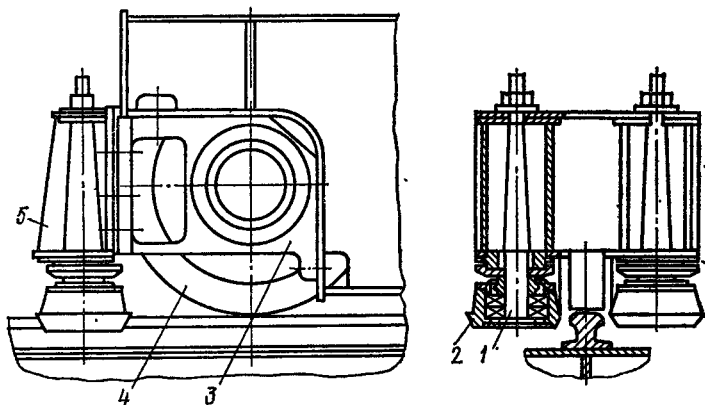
Установка безребордного ходового колеса механизма передвижения мостового крана [6]
